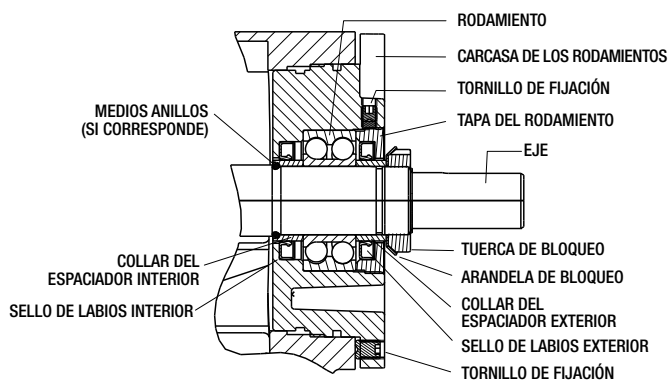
FIGURA G – ENSAMBLAJE DE LA CARCASA DE LOS RODAMIENTOS PARA G1-2 a G1-82
